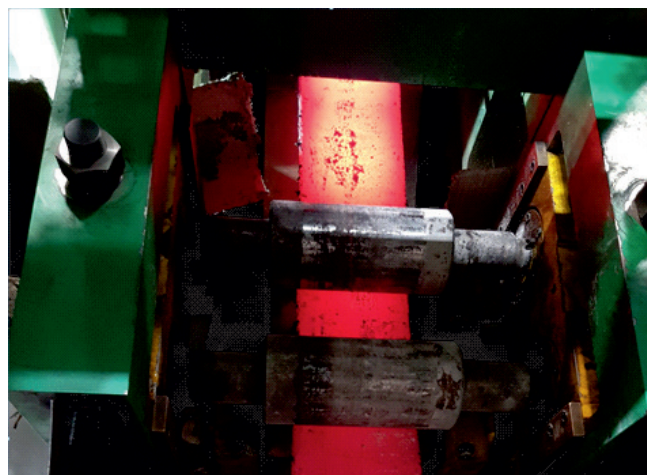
Вид полосы, вытягиваемой роликми тянущего устройства
